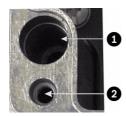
Schraubenlöcher für die Gehäusemontage, Schraubenlöcher für den Gehäusedeckel
